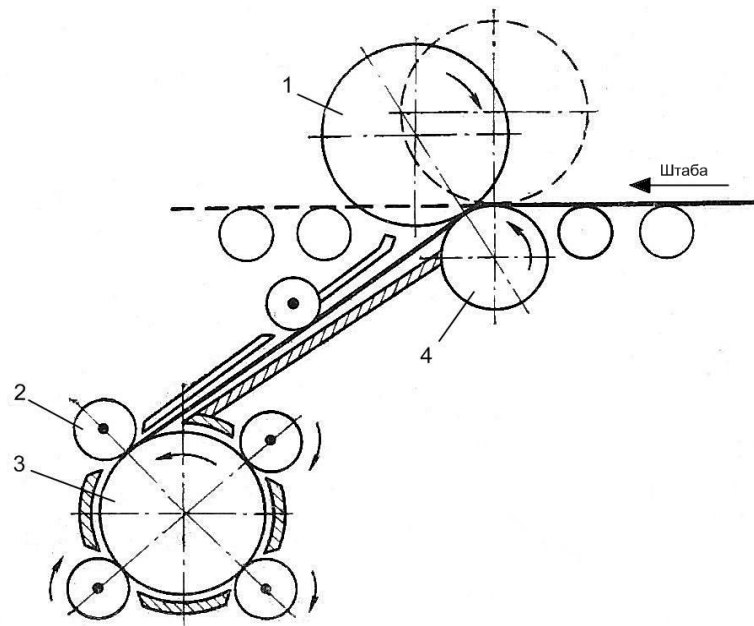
Барабанний змотувач з 4-ма роликами: 1 – верхній тягнучий ролик; 2 – формуючий ролик; 3 – барабан змотувача; 4 – нижній тягнучий ролик
